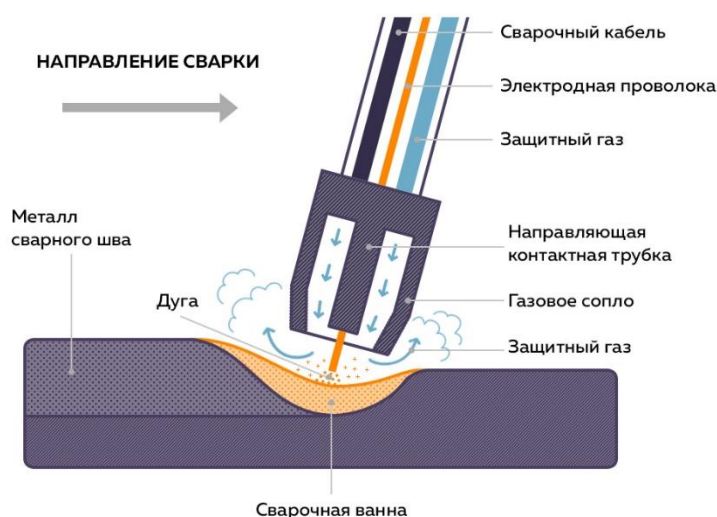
Схема выполнения механизированной сварки в защитных газах
